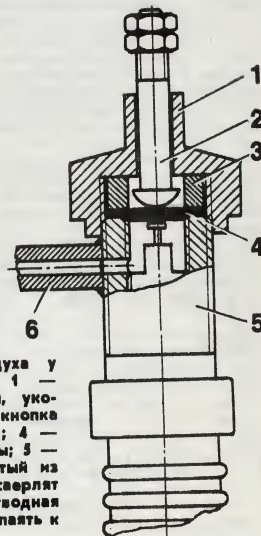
Клапан для воздуха у среднего пульверизатора: 1 — колпачок шпинного вентиля, укороченный «по месту»; 2 — кнопка включения; 3 — прокладка; 4 — прокладка из мягкой резины; 5 — вентиль с золотником, взятый из старой камеры (в нем сверлят отводное отверстие); 6 — отводная трубка, которую нужно припаять к вентилю.
